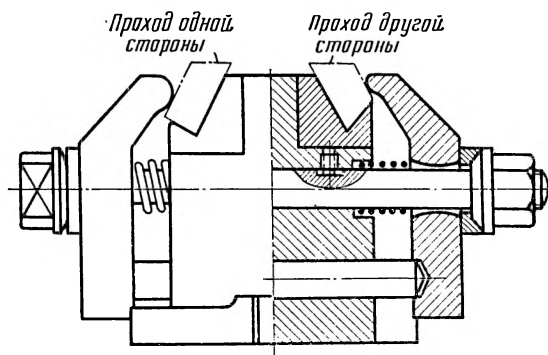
Приспособление для фрезерования тангенциальных резов с углом 60°
